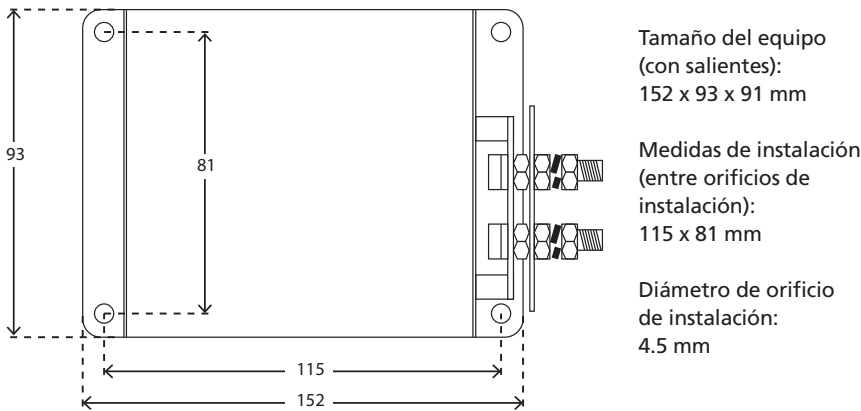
Dimensiones Generales y de Instalación para STEP 20.
